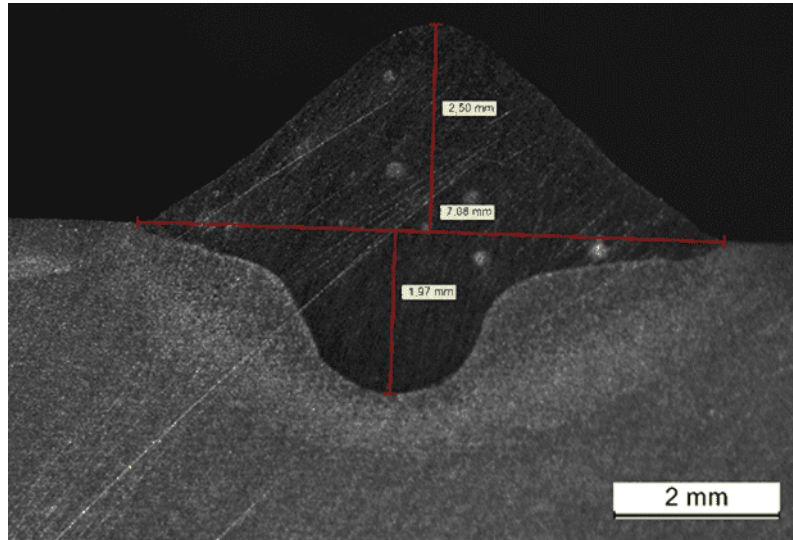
Imagem do cordão de soldadura depositado.
